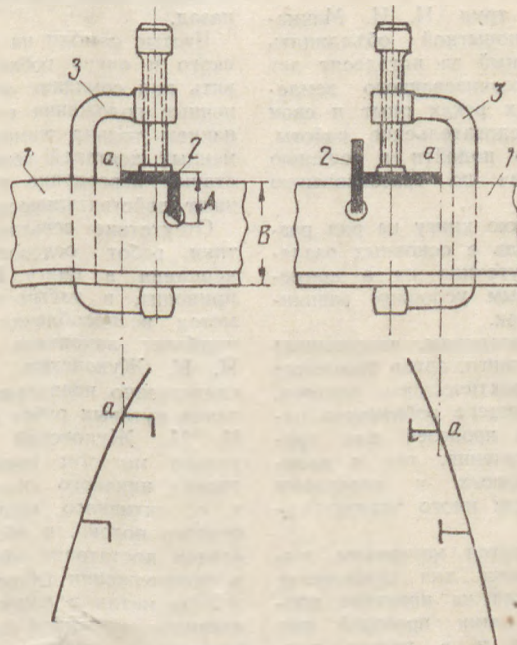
1 — рыбья или батокс кондуктора; 2 — шпангоутная рама; 3 — струбцина
